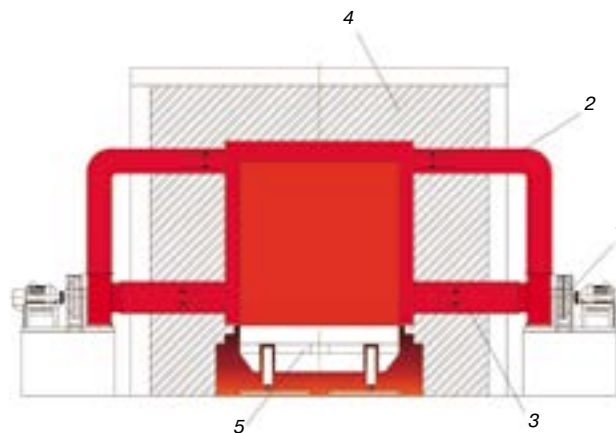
Вариант установки жарового вентилятора «Гелиотис» на печь: 1 – жаровый вентилятор; 2 – подающий трубопровод в печь; 3 – забор воздуха из печи; 4 – футеровка печи; 5 – вагонетка
